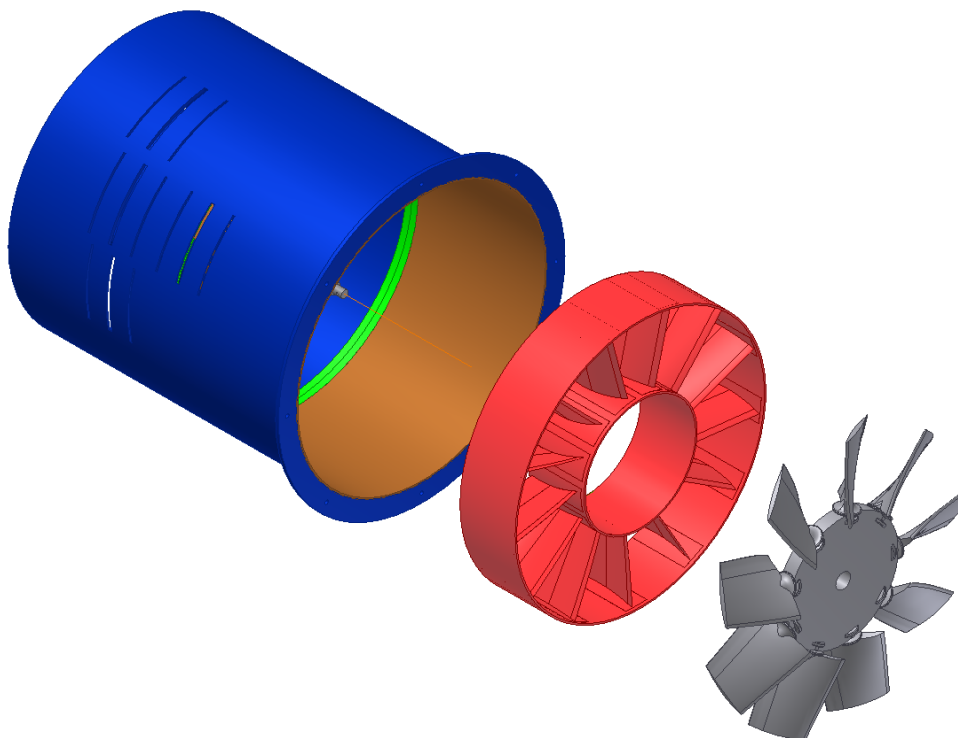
Montaje del rotor y el stator en la carcasa.
